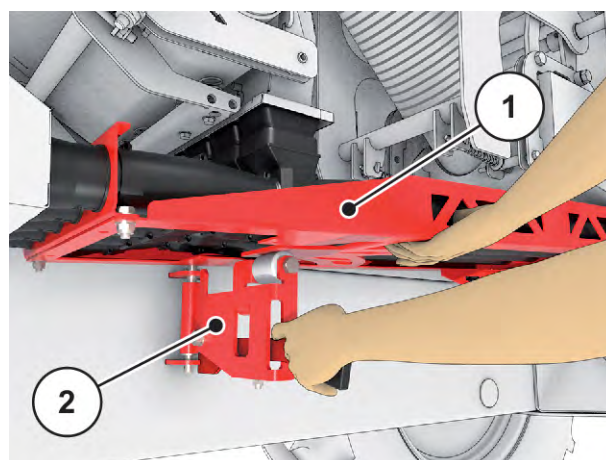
Déverrouillage du levier du support de la conduite d'air
